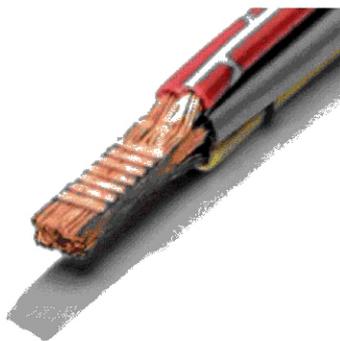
Одностороннее сваривание, полученное сваркой ультразвуком
